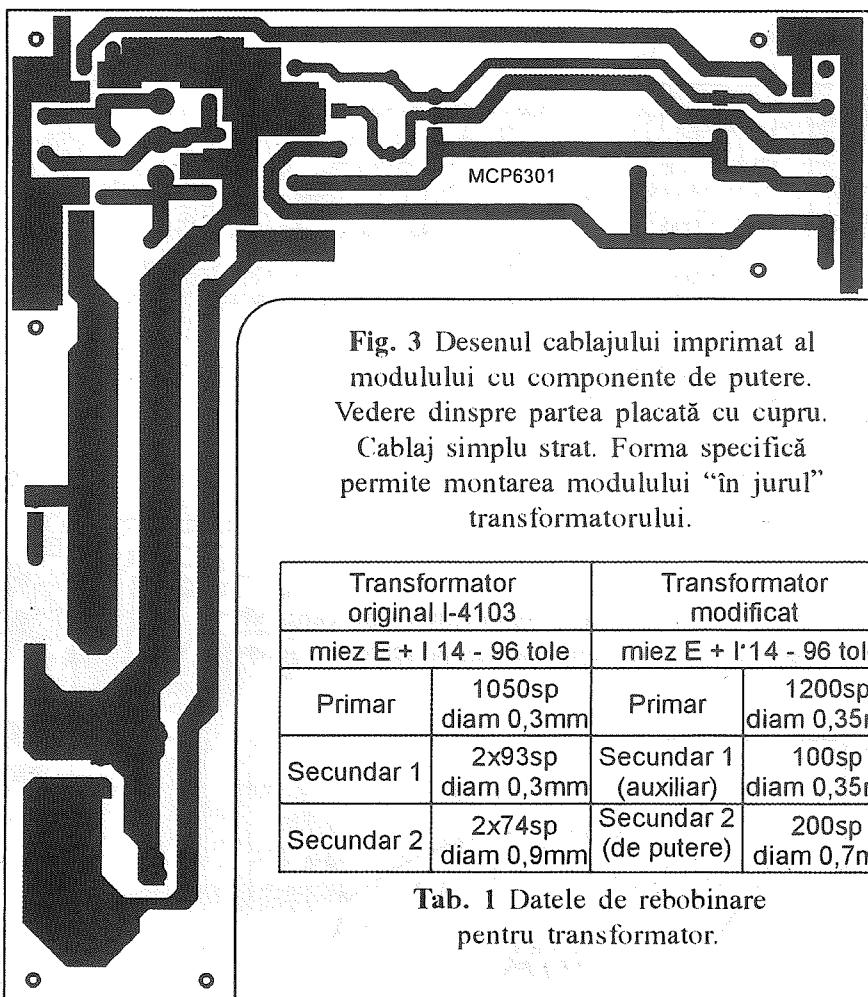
Desenul cablajului imprimat al modulului cu componente de putere. Vedere dinspre partea placă cu cupru.
